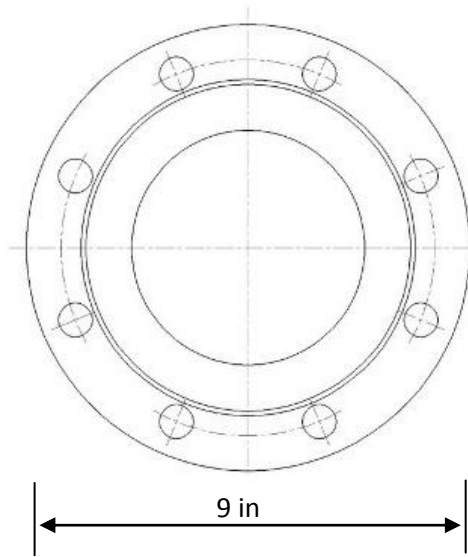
Plano del diseño de los bridas de la columna de destilación.
